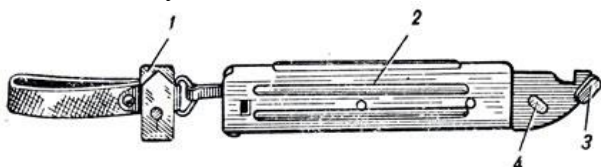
Ножны: 1 - подвеска с карабинчиками; 2 - пластмассовый корпус; 3 - упор; 4 - выступ-ось
